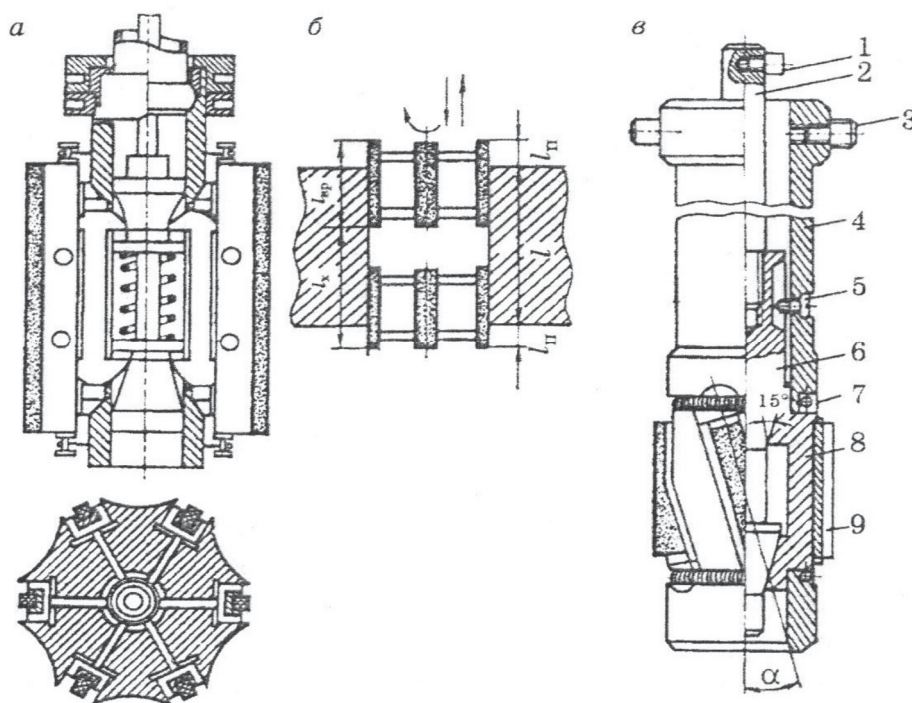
Хонинговальная головка: *а* – конструкция; *б* – схема определения длины перемещения головки; *в* – головка для хонингования шлицевого отверстия: 1, 3 – шпильки; 2, 6 – штоки; 4 – корпус; 5 – шуруп; 7 – пружина; 8 – колодка; 9 – брусок
